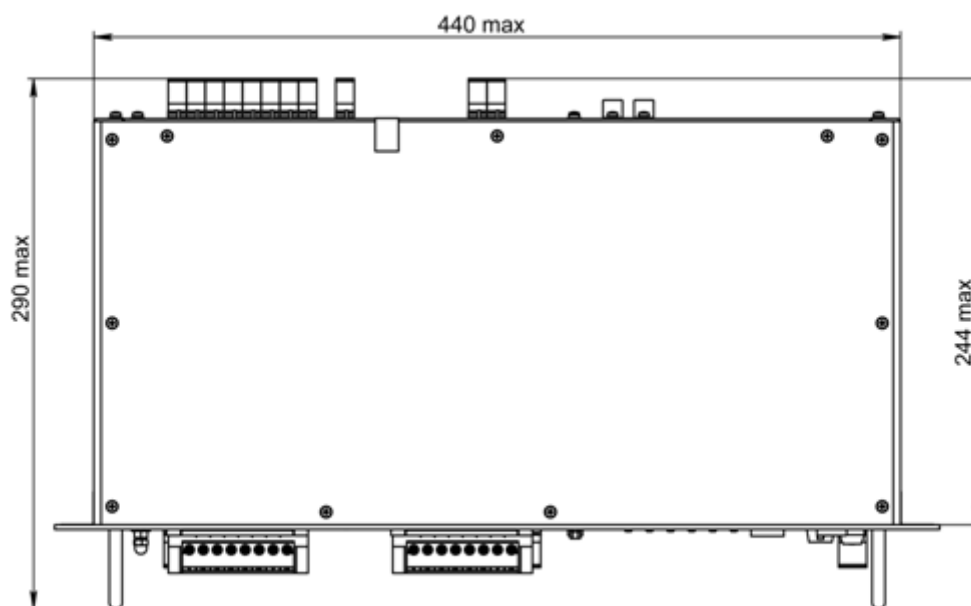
Габаритные размеры регистратора вид сверху
